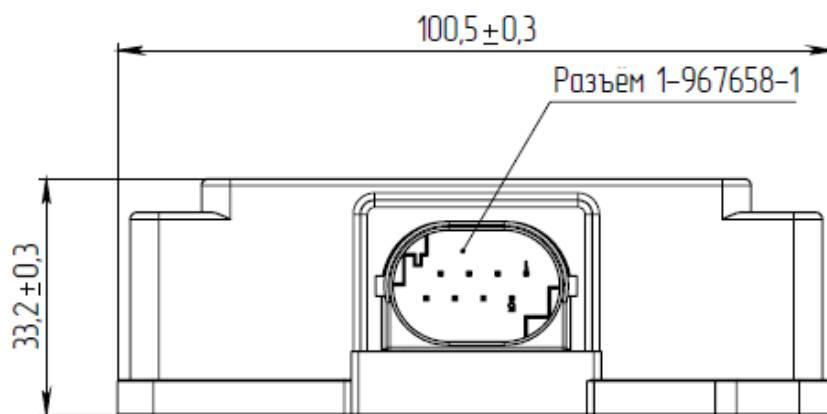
Габаритные размеры исполнений изделия ТСКЯ.466369.007, ТСКЯ.466369.007-01, маркировка, расположение отверстий для крепления (лист 1 из 2)
